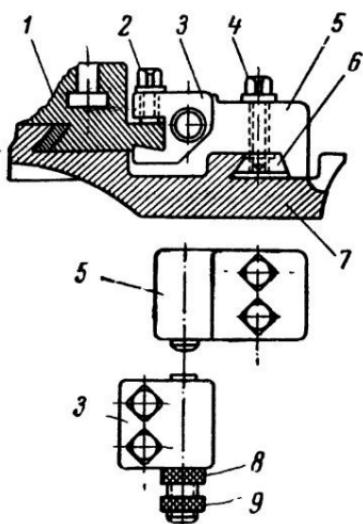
Однопозиционный упор для поперечных салазок суппорта: 1 — поперечные салазки суппорта; 2 — болт крепления упора; 3 — корпус упора; 4 — болт крепления колодки; 5 — колодка; 6 — клин; 7 — салазки суппорта; 8 — контргайка; 9 — болт-упор.
